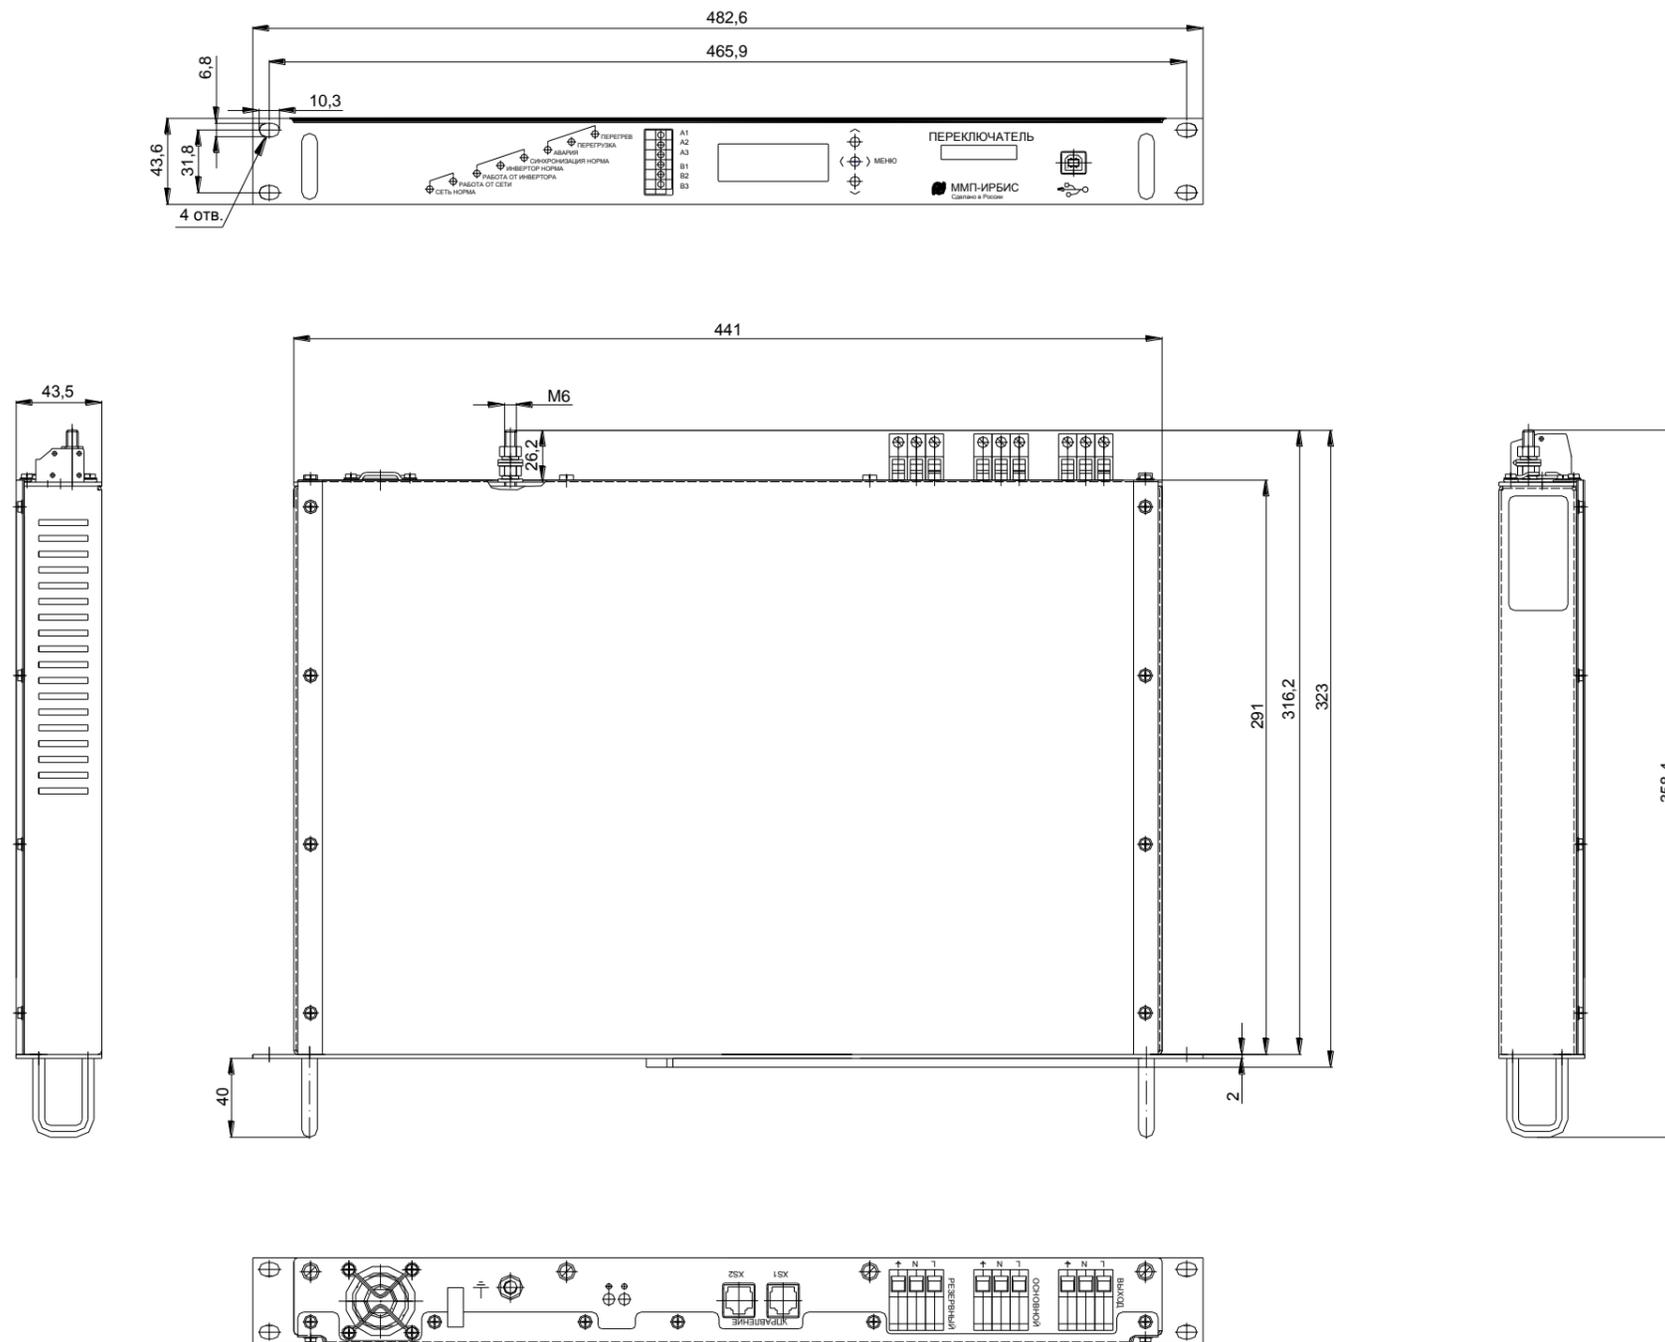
Габаритный чертеж на ПЭС 3000, ПЭС 7500, ПЭС 9000
